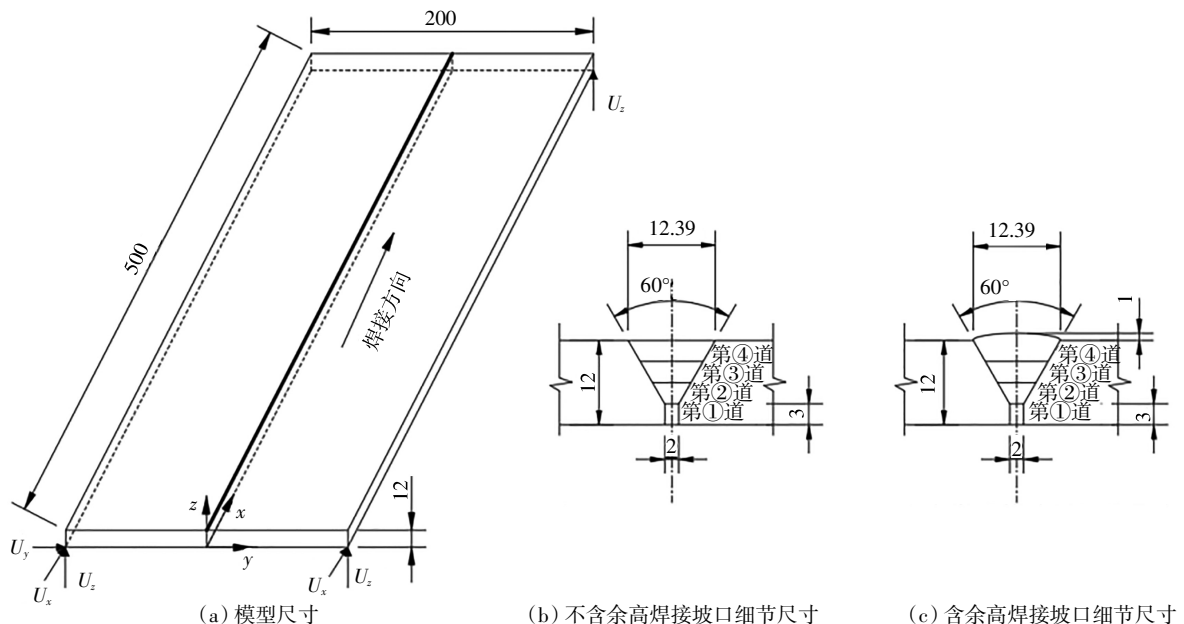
钢板试件模型及焊接坡口尺寸(单位:mm)
